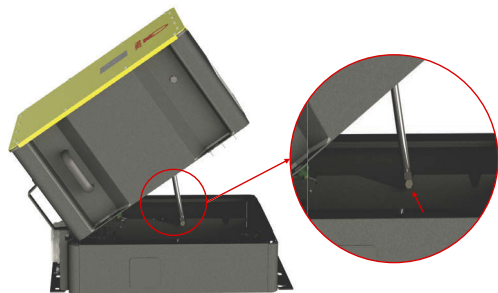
Abstützen des Hydraulikdämpfers in die Aussparung der Connection Box bei horizontaler Montage
